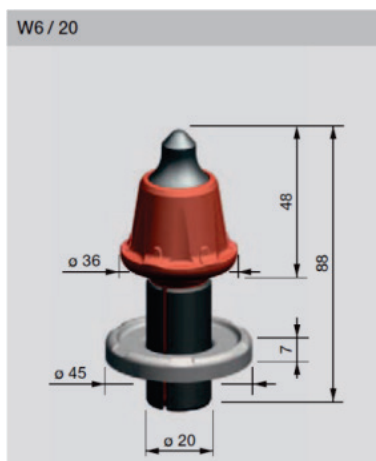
Дорожный резец W6/20 фирмы Wirtgen
